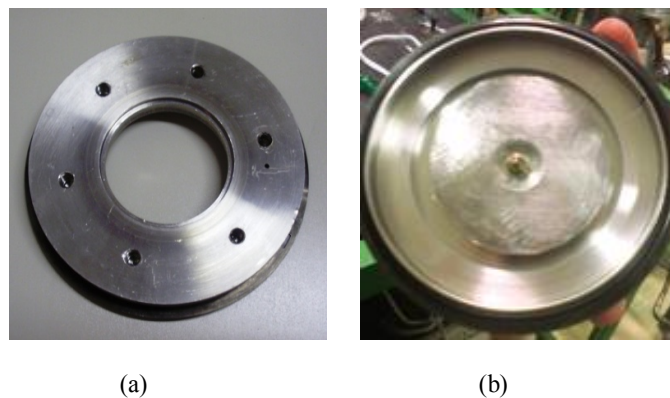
a) Flange de adaptação; b) conjunto formado pelos dois flanges do sistema de detecção (flange com passador elétrico fixo e flange de adaptação) com o anteparo B conectado
